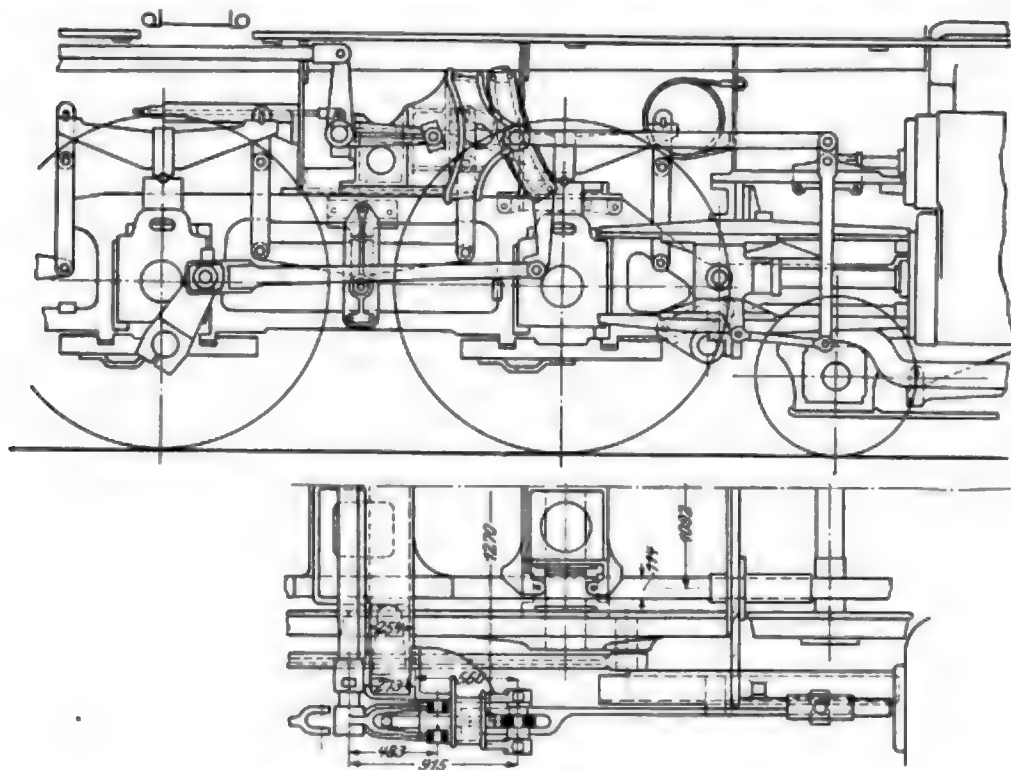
und 2. Amerikanische Heusinger-Steuerung.
